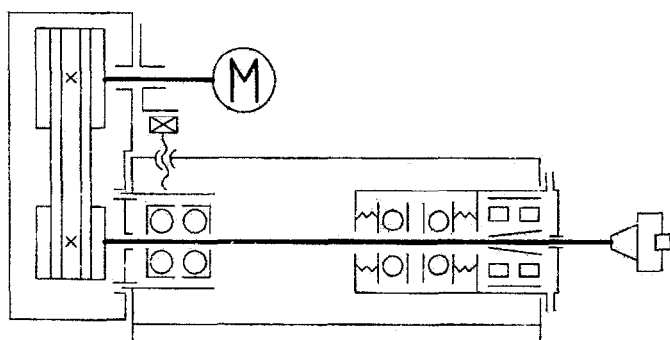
Кинематическая схема горизонтальной фрезерной бабки агрегатного станка
